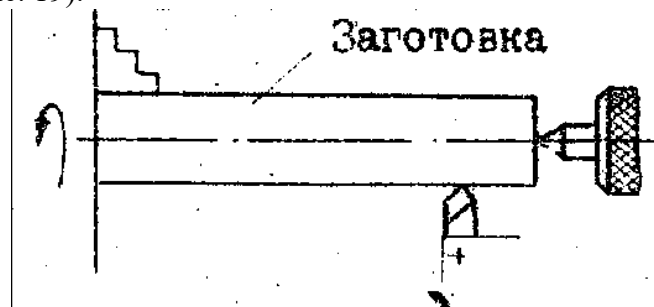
Закрепление длинной заготовки в патроне с поддержкой задним центром.
